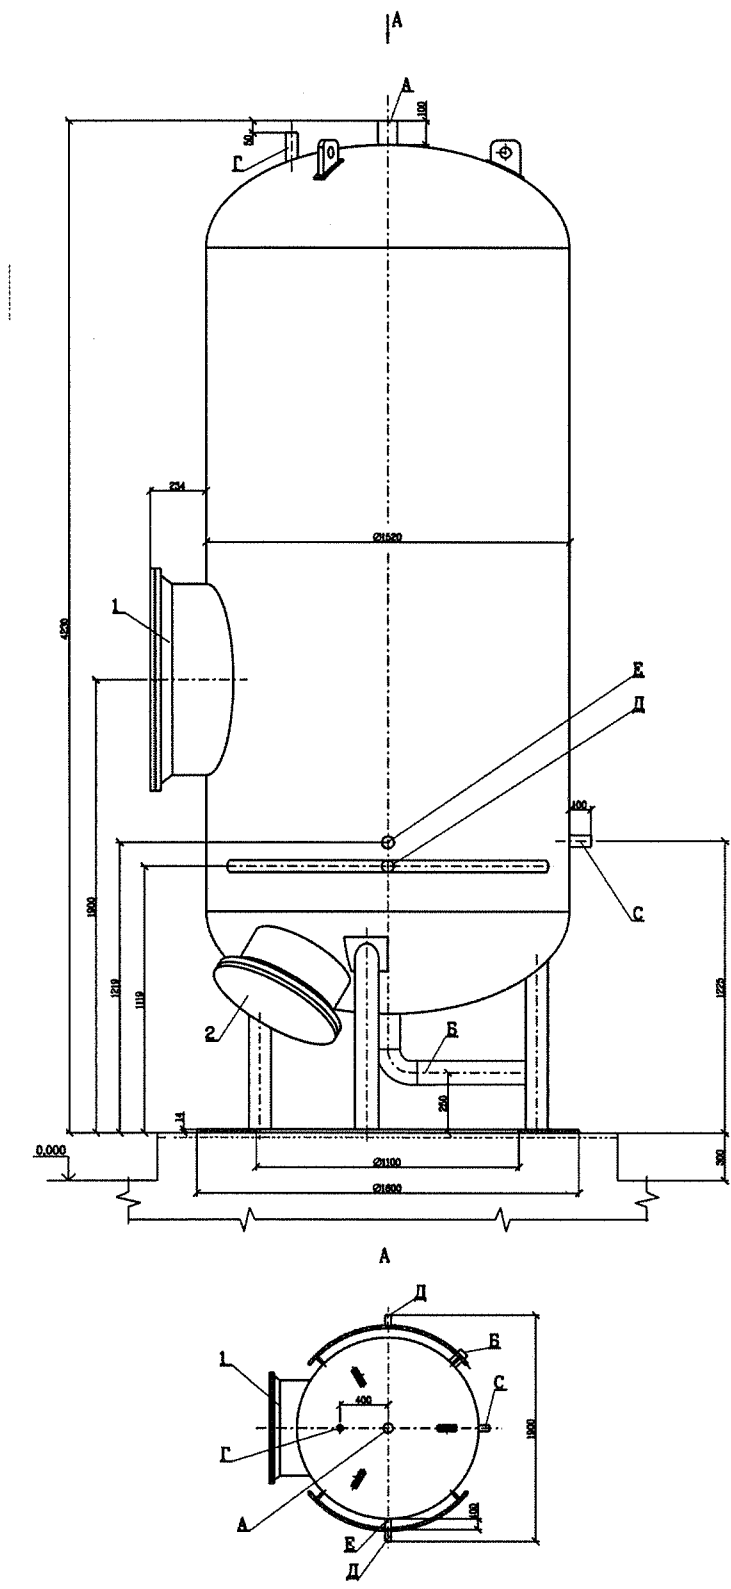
Габаритный чертеж фильтра ионитного KBF50AT001
